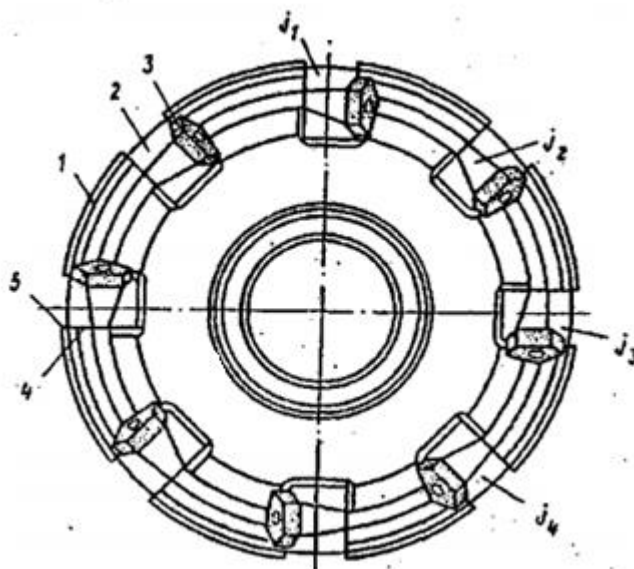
Фреза із зубами із змінною жорсткістю
